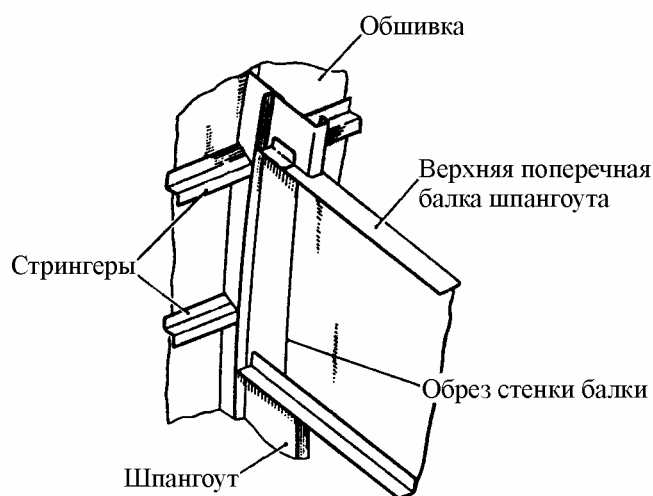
Крепление поперечной балки к ободу шпангоута
